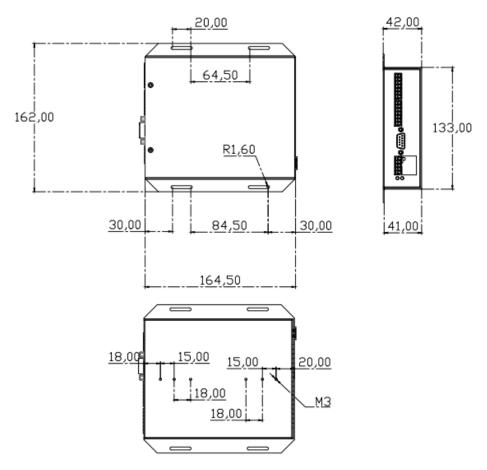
Размеры основного блока контроллеров THC F1628S/F1628D.
